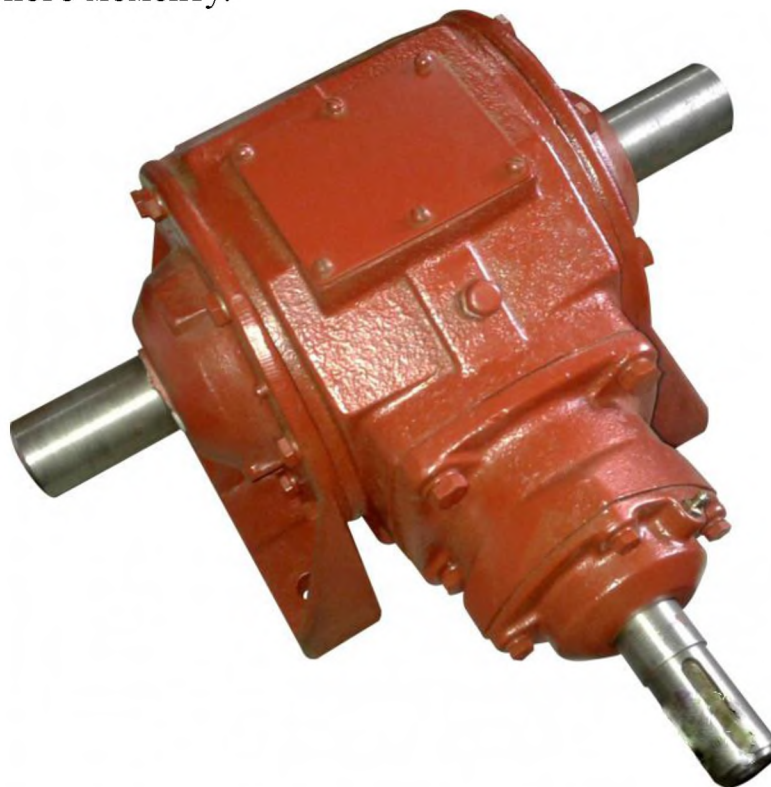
Конічний одноступінчастий кутовий редуктор
